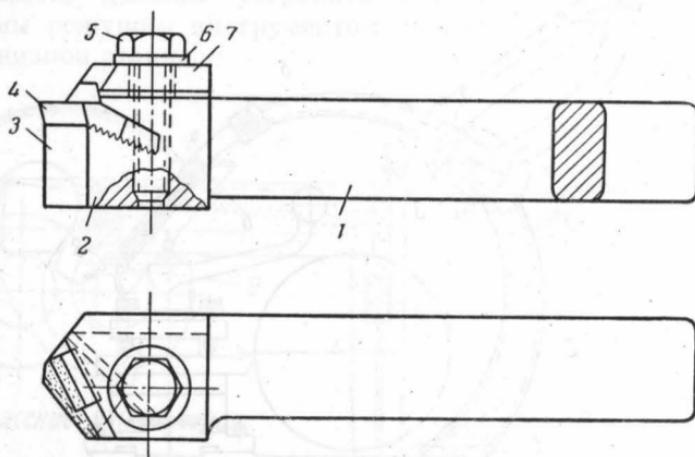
Резец с механическим креплением режущих пластин и стружкодробящих порогов конструкции Д. И. Рыжкова:
